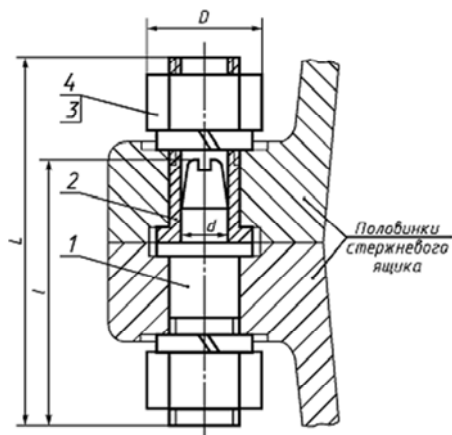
Конструкция соединения штырями и втулками с резьбовыми хвостовиками
